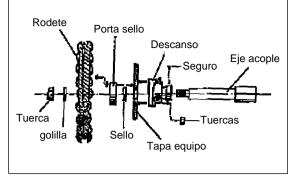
Vista en explosión del conjunto Rodete-Eje
